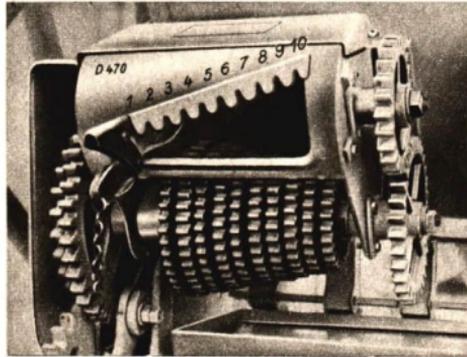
/3. Vielstufenge triebe einer Drillmaschine
